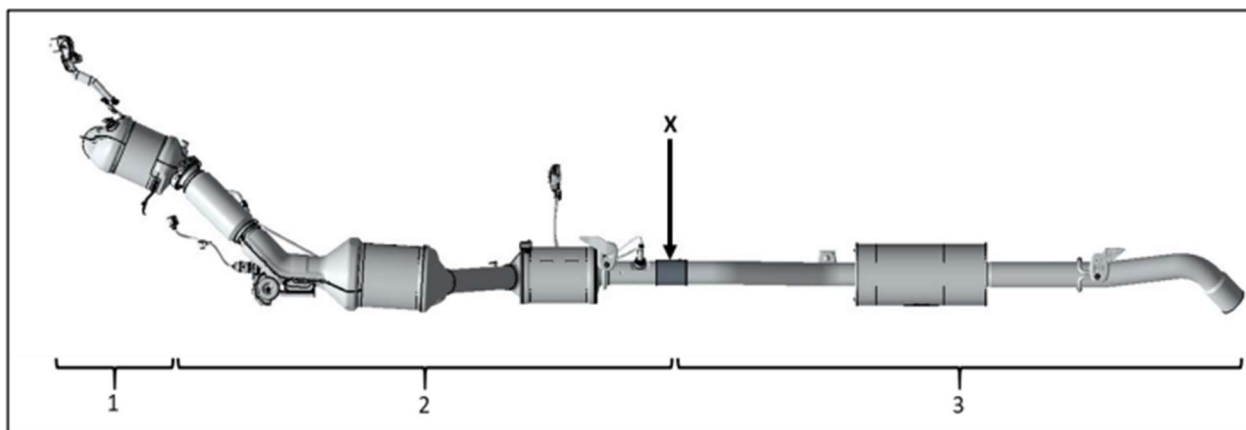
Výfukový systém přední část (první obr.) a zadní tlumič (druhý obr.) (motor: přední příčné uložení)
